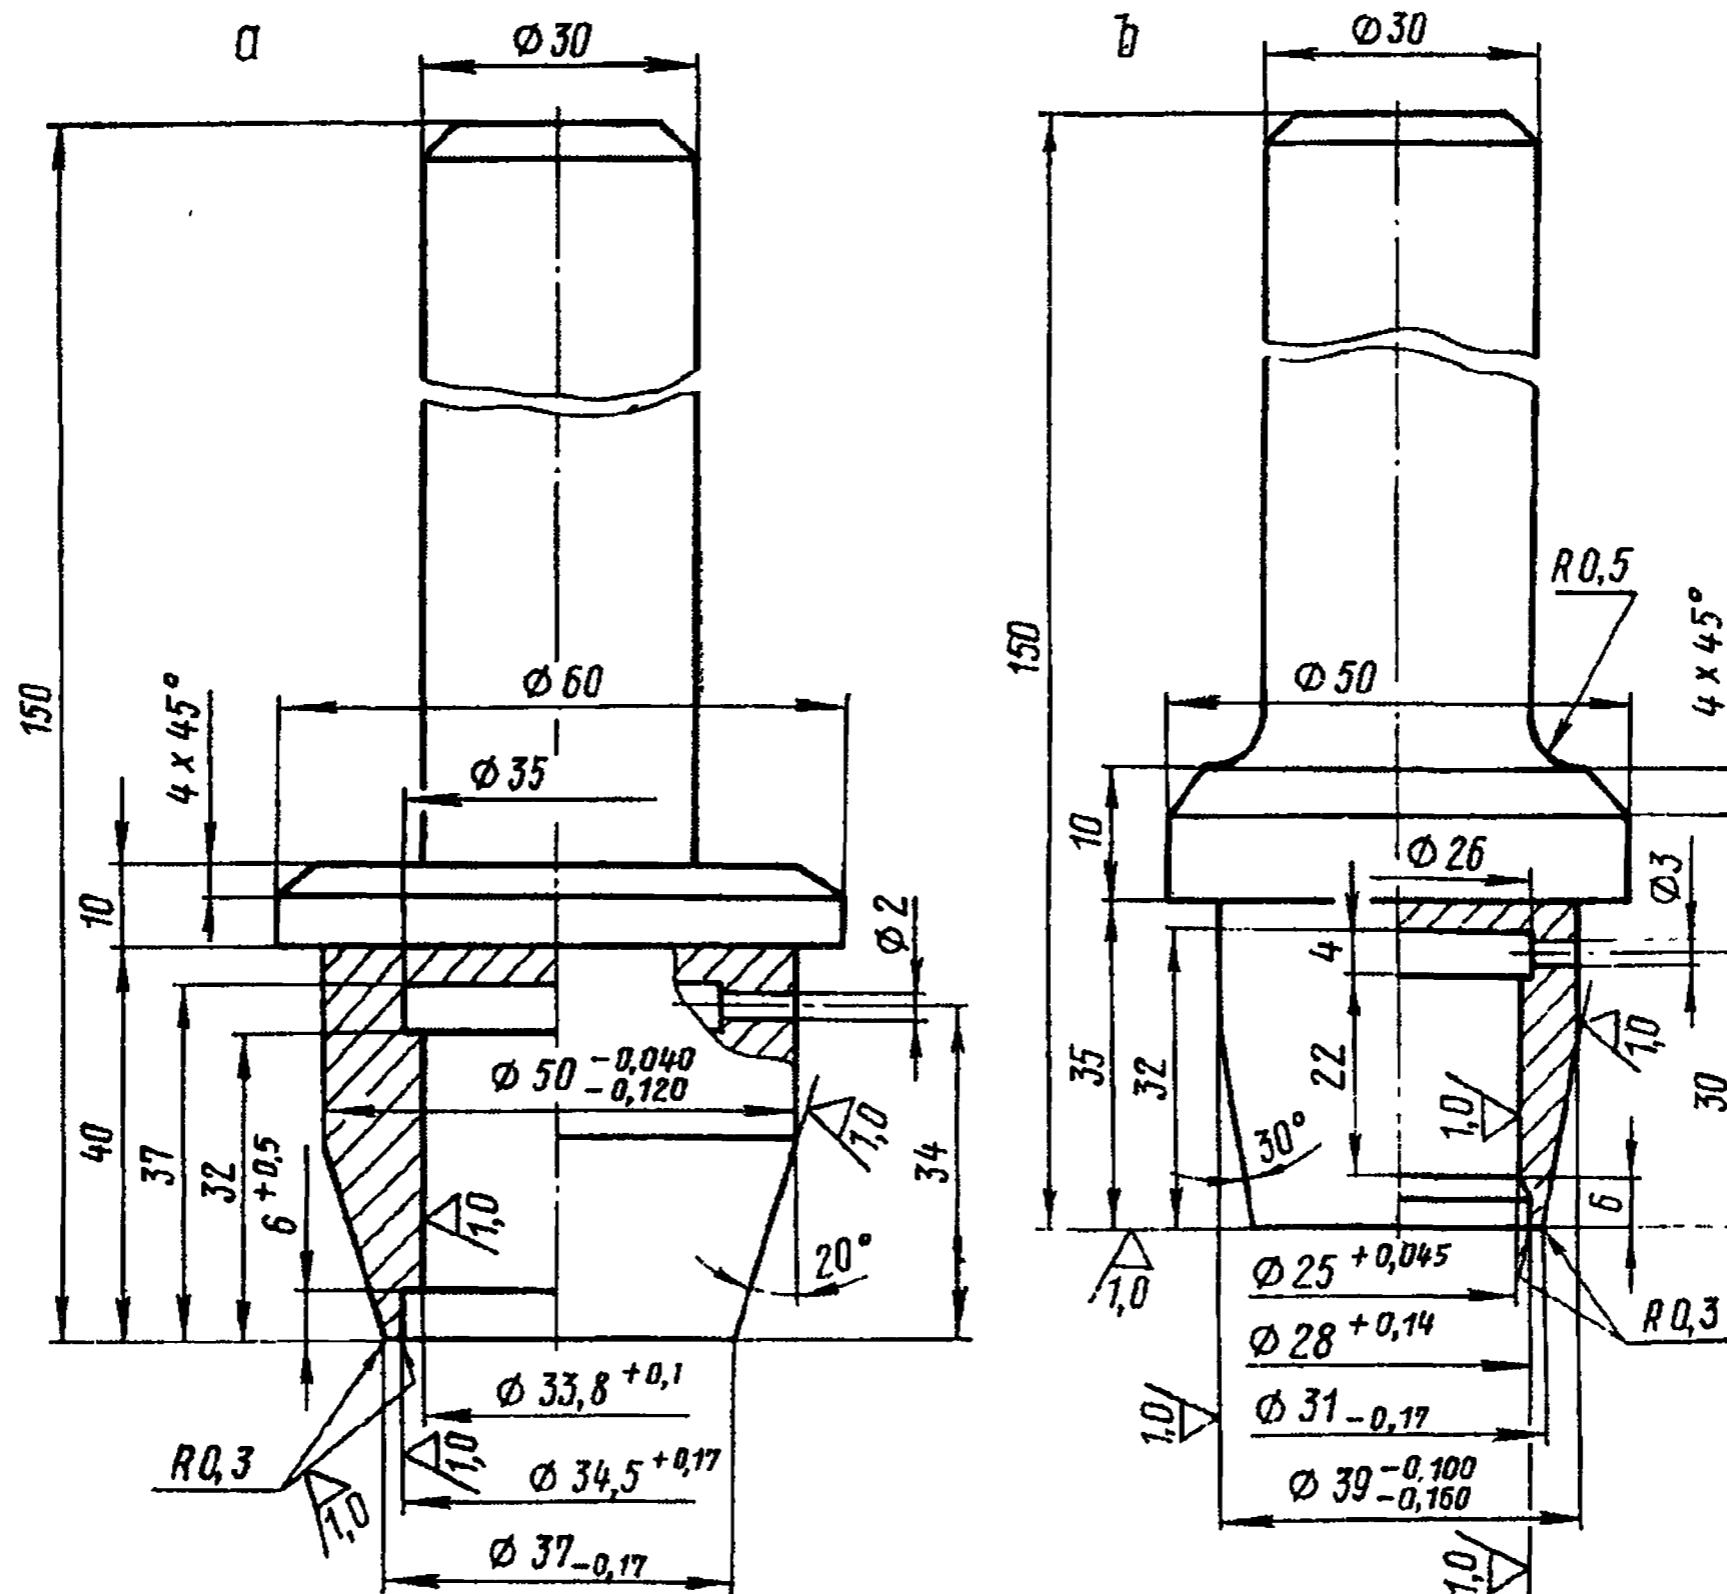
Оправки для напрессовки торцовых уплотнений на крестовины карданных валов приводов:
